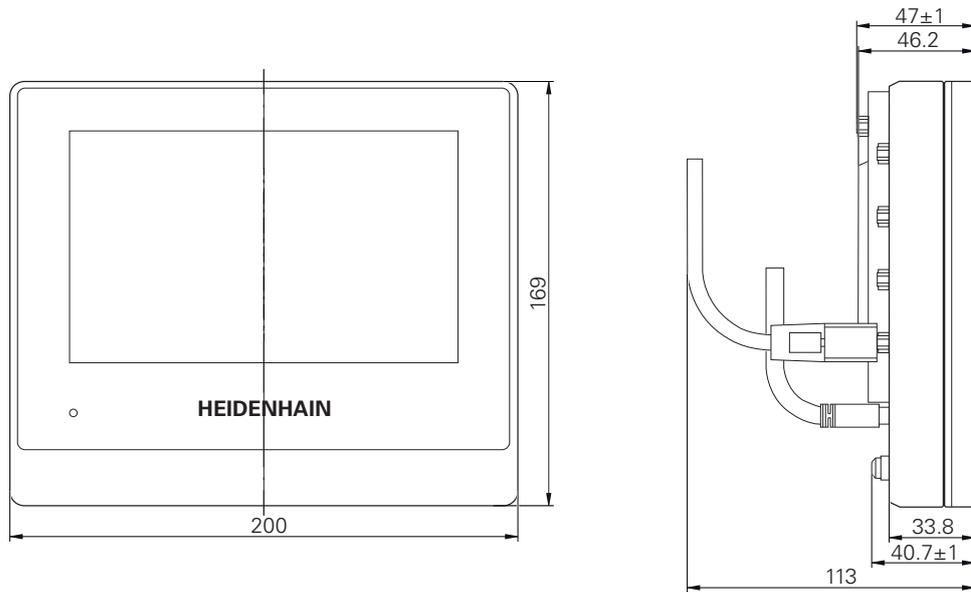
Dimensions du carter des appareils portant l'ID 1089182-xx
